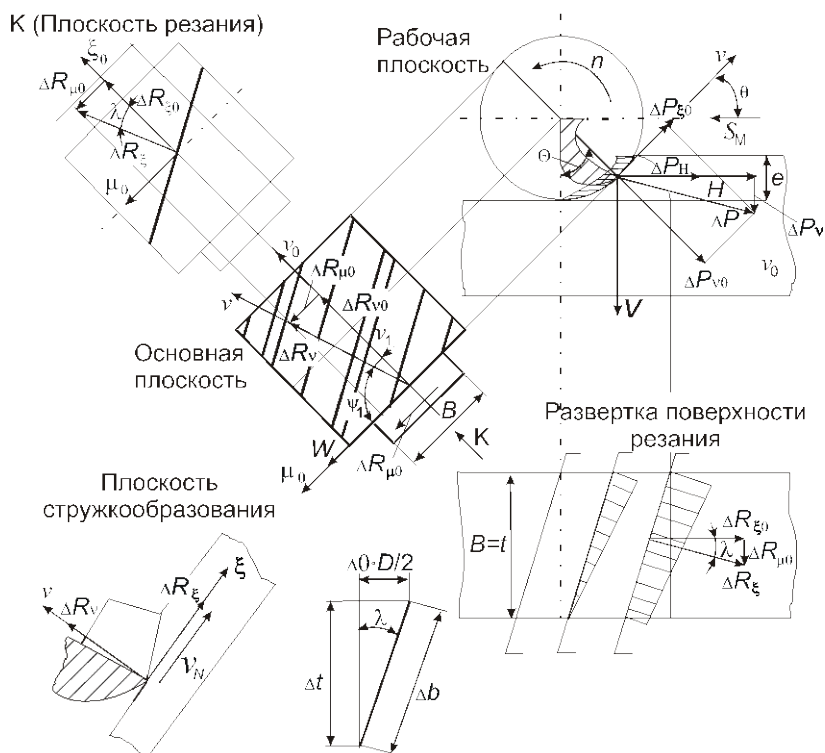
Схема технологических осей и приращений сил при встречном фрезеровании цилиндрической фрезой с винтовыми зубьями
